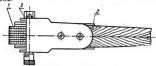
Державка с набором шарошек-звездочек для правки шлифовальных кругов:
